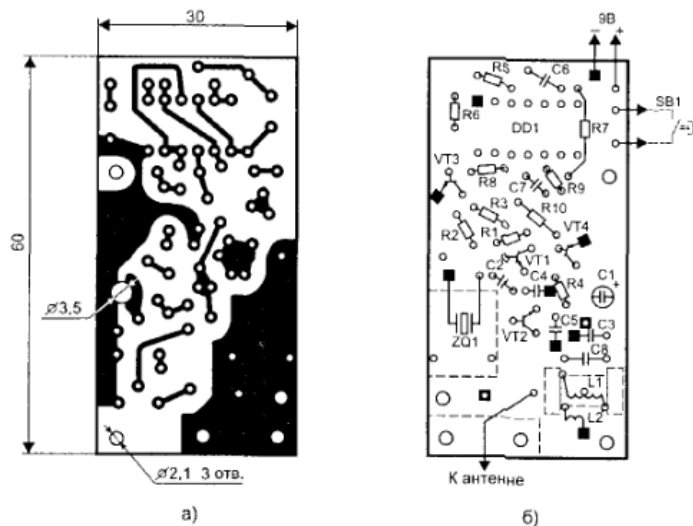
Передатчик: а — печатная плата; б — расположение деталей
